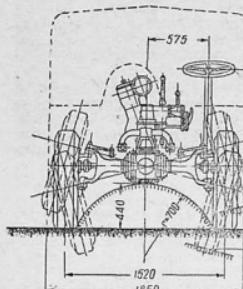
Клиренс увеличивается при установке дополнительного редуктора в ступице колес (автомобиль Зауэрса)
